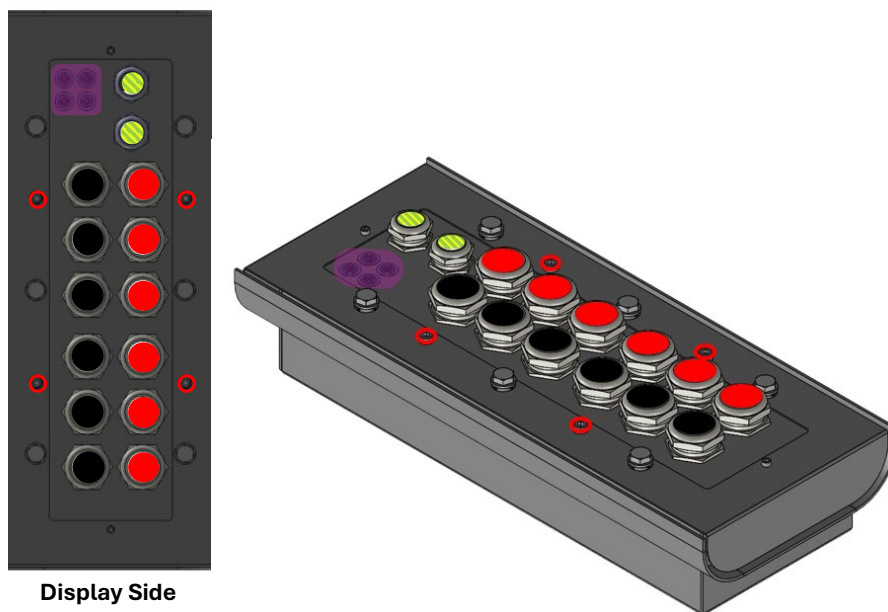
EV-Dispenser Kabeleinführungsplatte mit Kabelverschraubungen
